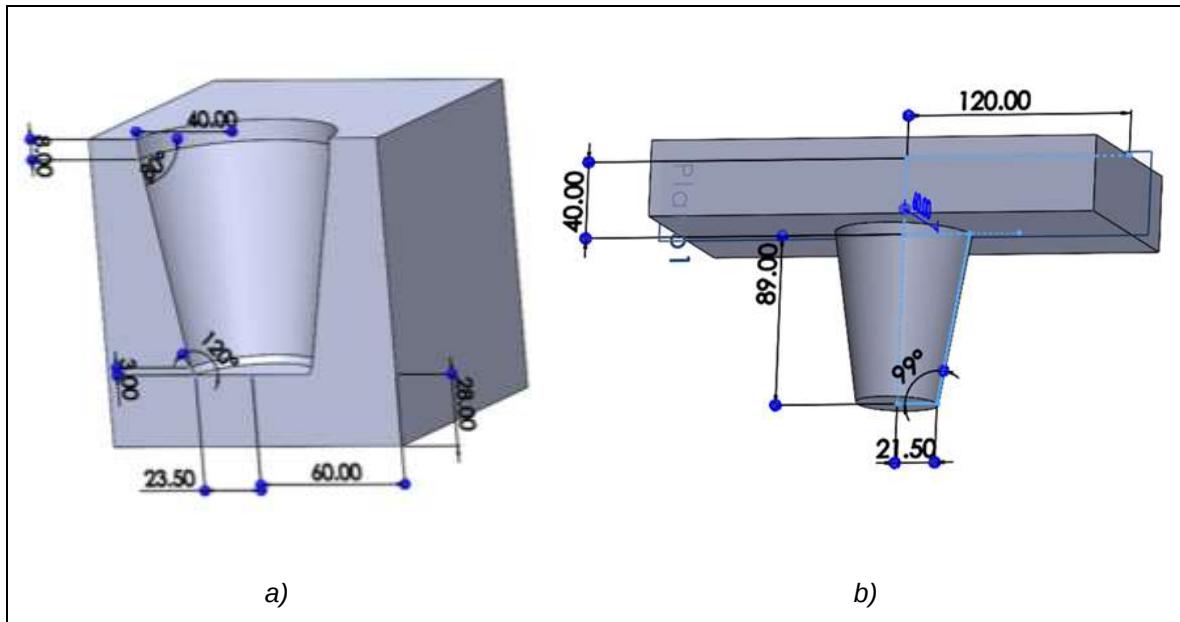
Dimensiones en mm del a) lado A y b) lado B del molde para formación de los vasos.
